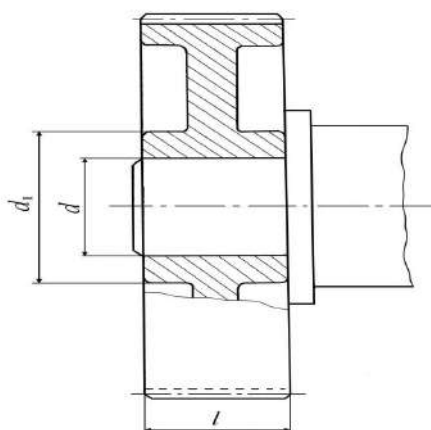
Расчетная схема напрессовки шестерни на распредвал
